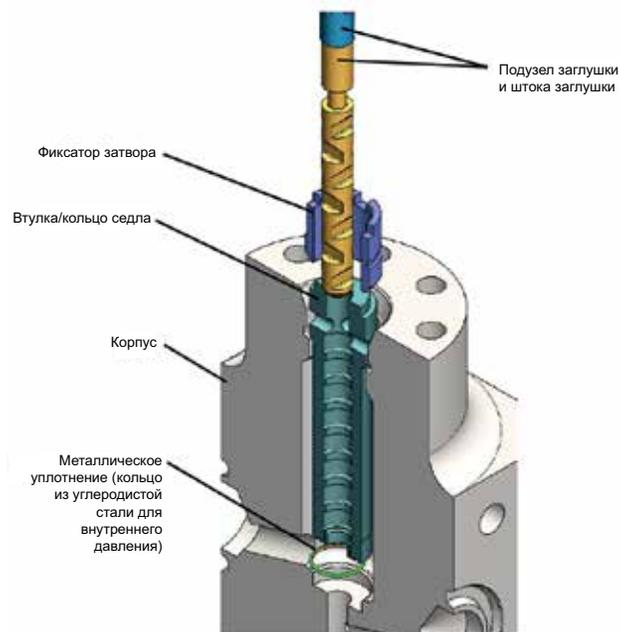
Развернутый вид затвора в сборе - Узел втулки/кольца седла (несбалансированное, 1")
